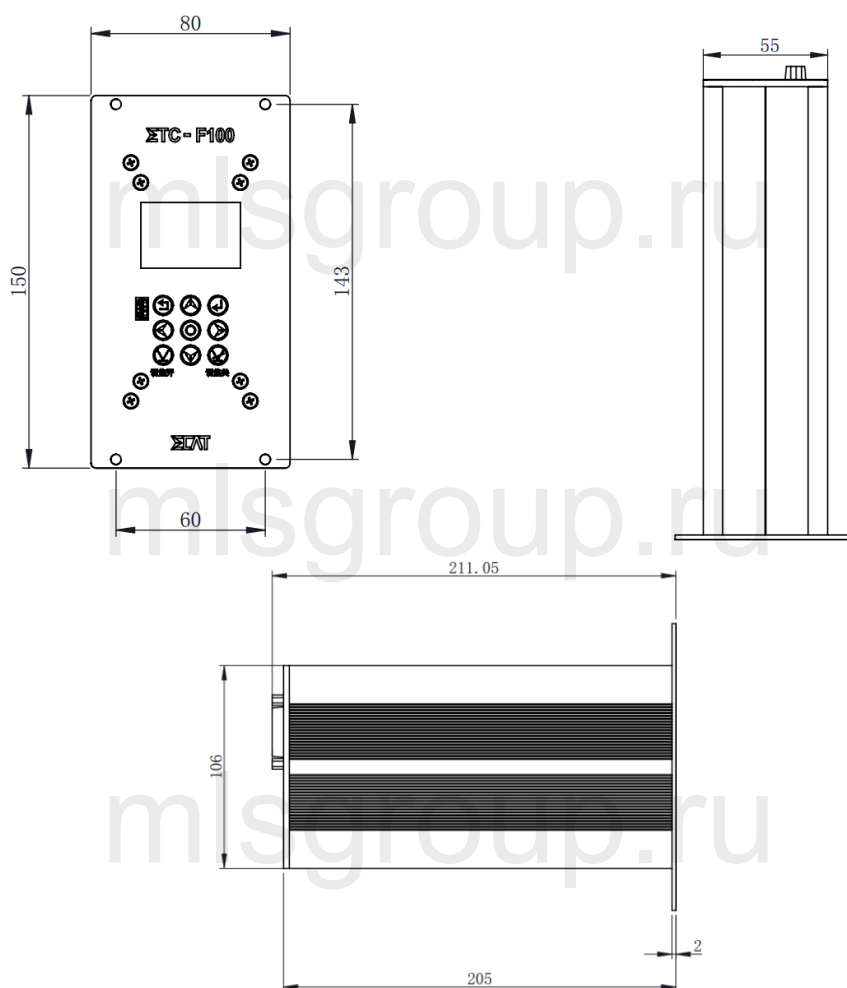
Габаритные размеры контроллера ETC-F100 (мм)
